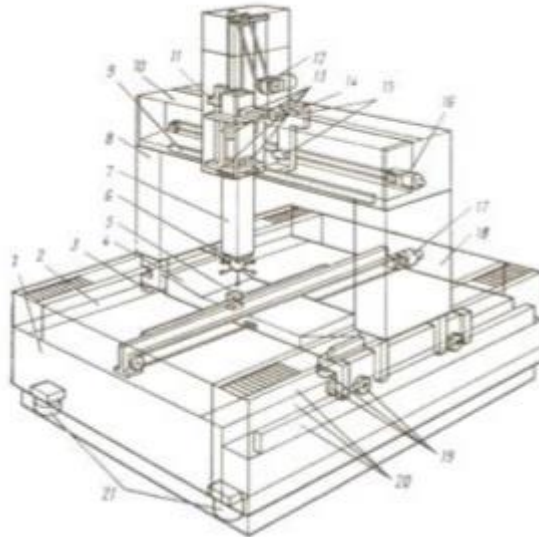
Схема базової частини КВМ - основа; 2,20 - напрямні основи; 3,19 - підшипники порталу; 4, 8, 10, 18 - замикаючий місток, стійки і балка порталу; 5, 9, 11 - ПП порталу, каретки, пінолі; 6 – вимірювальна головка; 7 - піноль; 12, 16, 17 - приводи пінолі, каретки порталу; 13, 15 - підшипники пінолі і каретки; 14 - каретка; 21 - віброізолюючі опори.
